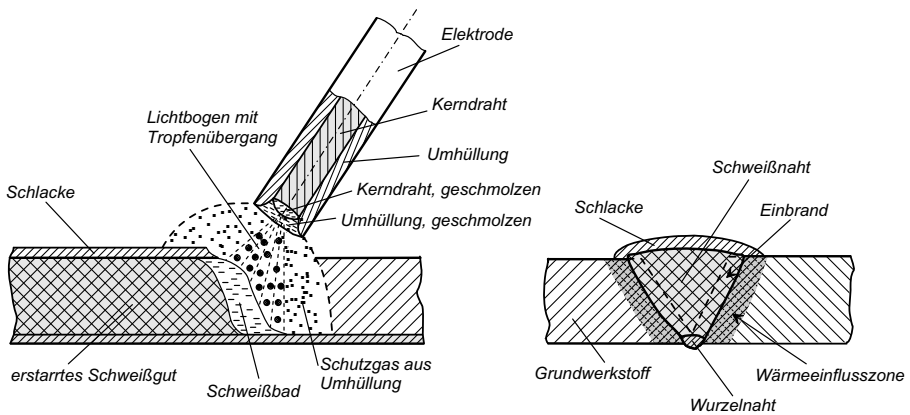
Lichtbogenhandschweißen
